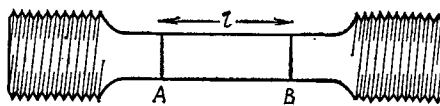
Стандартный круглый образец для испытания на растяжение;
